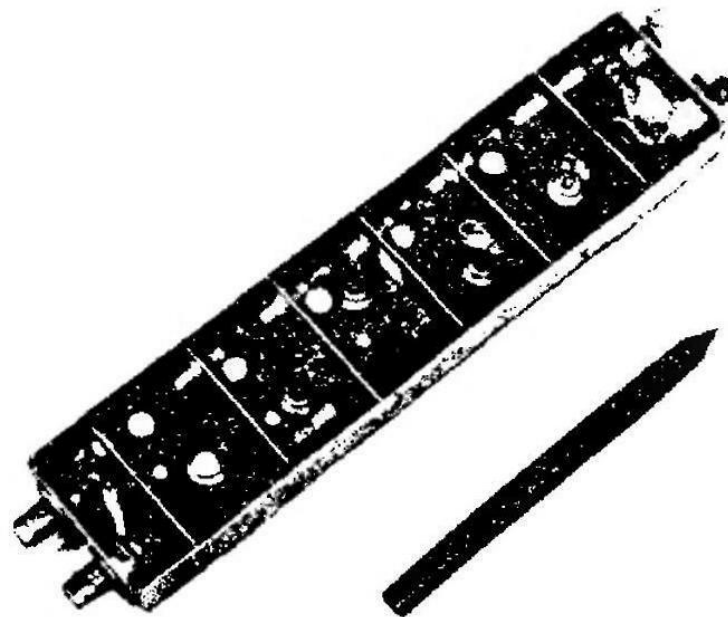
Конструкция усилителя (вид со снятой крышкой)
